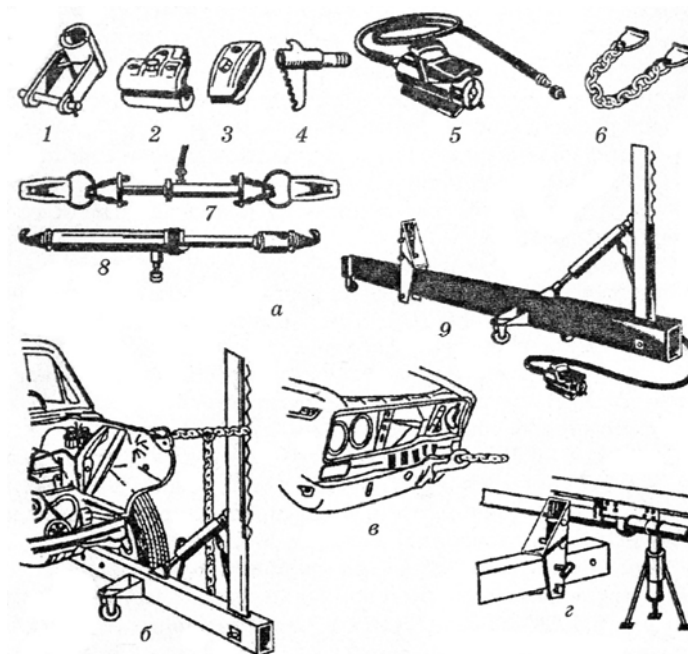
Приспособления для выполнения правки деформированного участка кузова:
